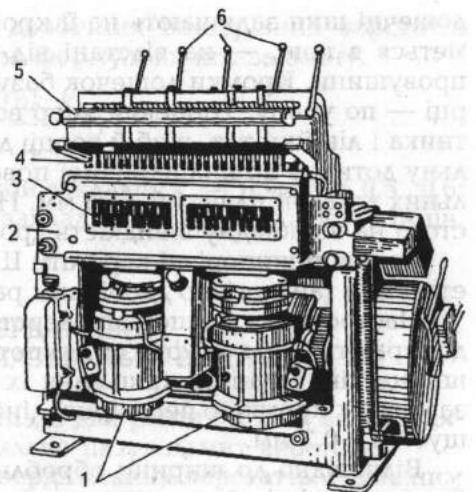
Шипорізний верстат для зарізування шипів "ластівчин хвіст" ШЛХ-3:
